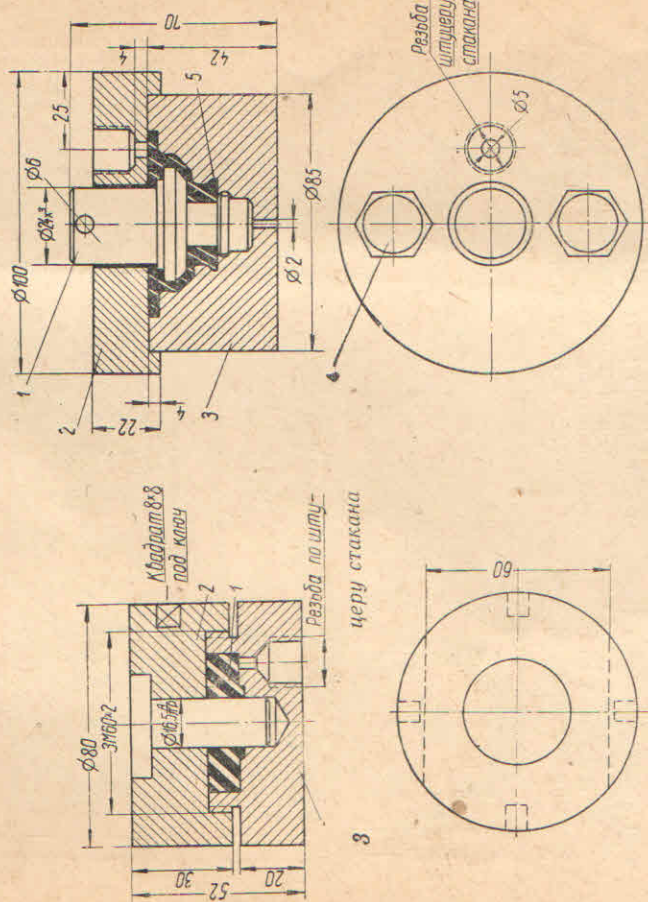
Пресс-форма в сборе с деталью № 20—1302045 — подушка подвески радиатора:
